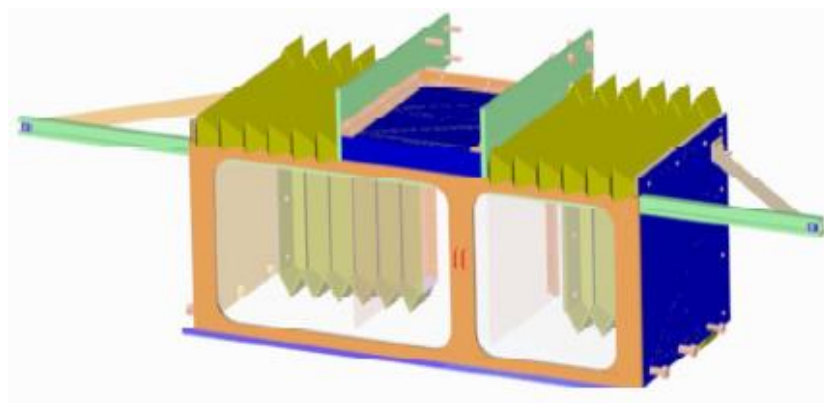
Ограждение фрезерно-сверлильных станков
